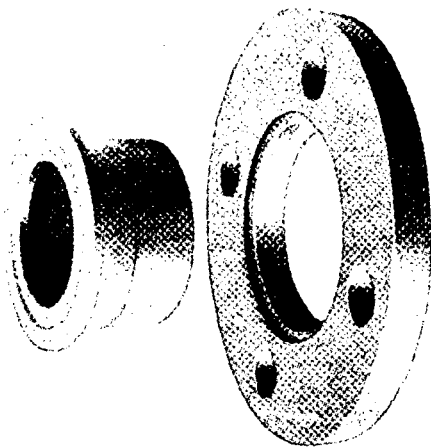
Flange livre e luva com ressalto cônico de PVC. (91*)
